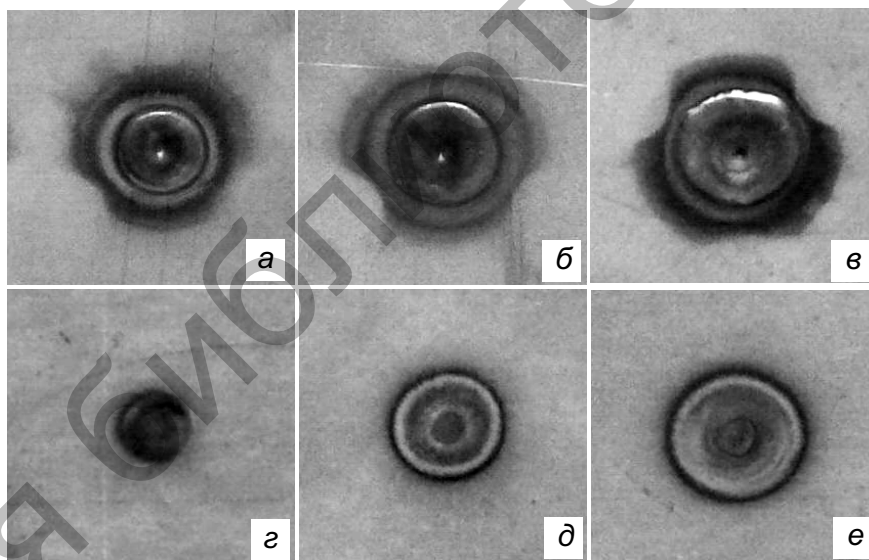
Влияние сварочного тока на внешний вид сварных точек:
